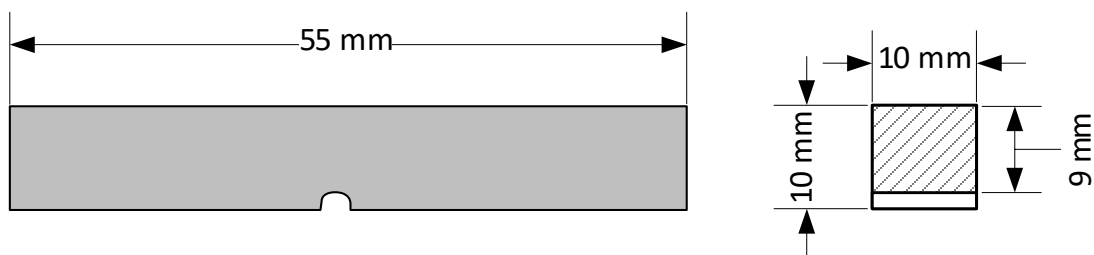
Dimensiones de la probeta del ensayo Charpy.
